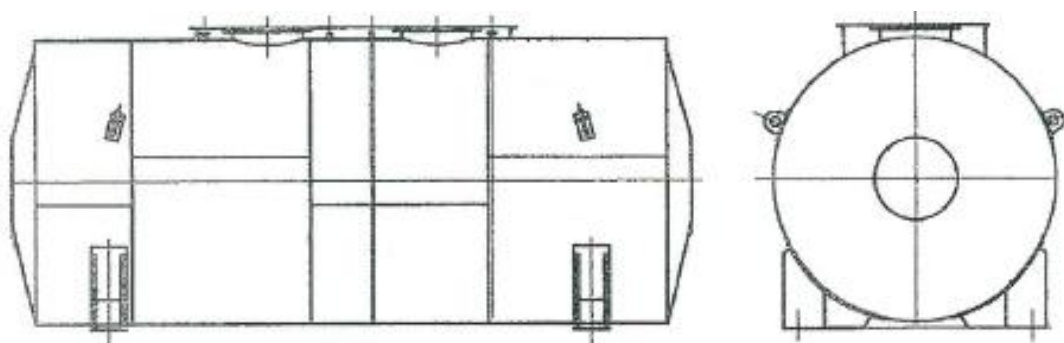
Общий вид эскиза резервуара РГС-25
